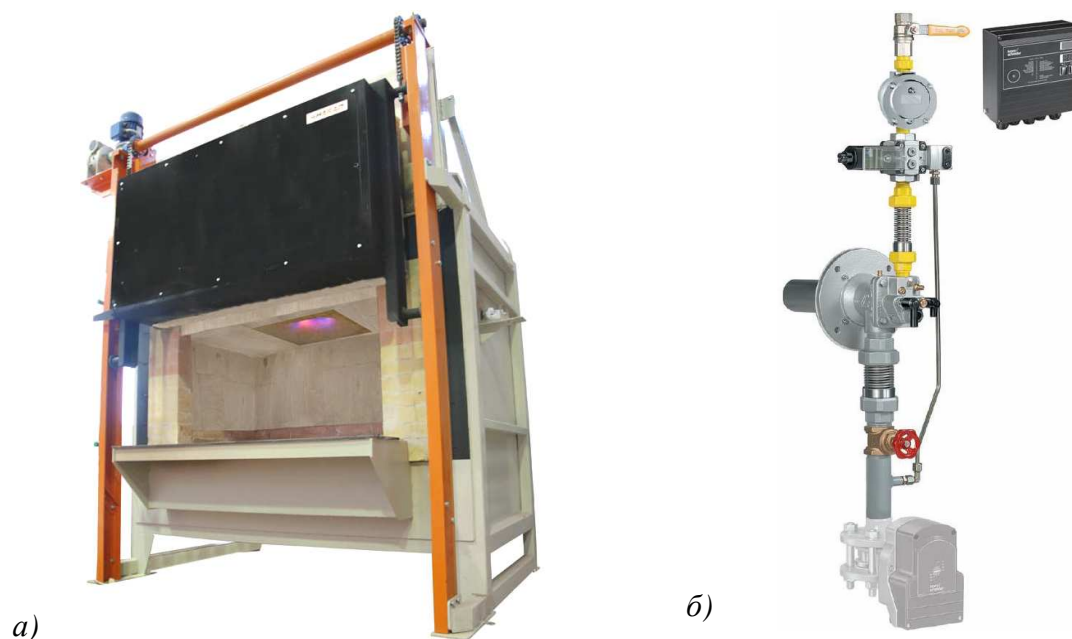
Фотография газовой кузнечной печи (а) и газовой горелки к ней (б)
